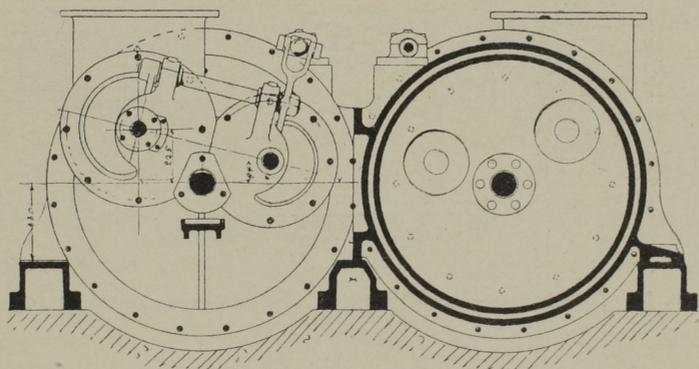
Stirnansicht und Querschnitt der Windcylinder.
